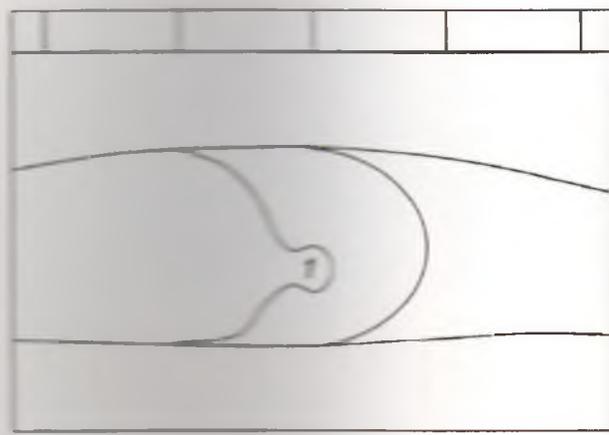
Наплыв – дефект в виде металла, вытекшего в процессе сварки на поверхность ранее выполненного участка шва и несплавленного с ним
